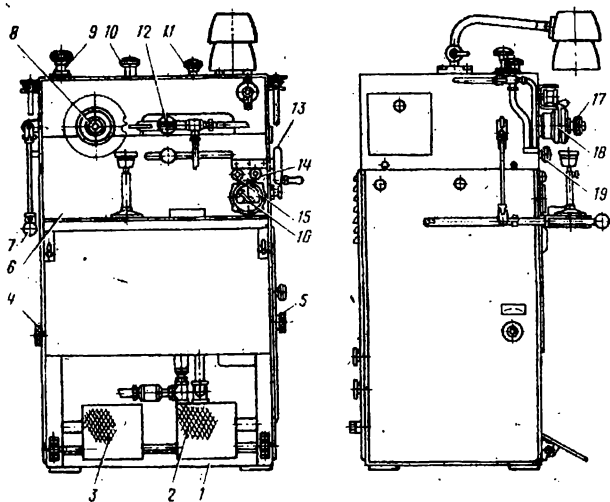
Установка НПЭ-05У для электроконтактной напайки пластинок твердого сплава
